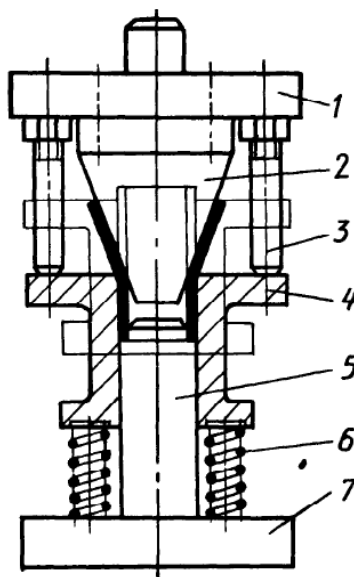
Схема штампа со скользящей втулкой-подпором: 1 – верхняя плита; 2 – пуансон; 3 – толкатель; 4 – скользящая втулка; 5 – опорный стержень; 6 – пружина; 7 – нижняя плита
